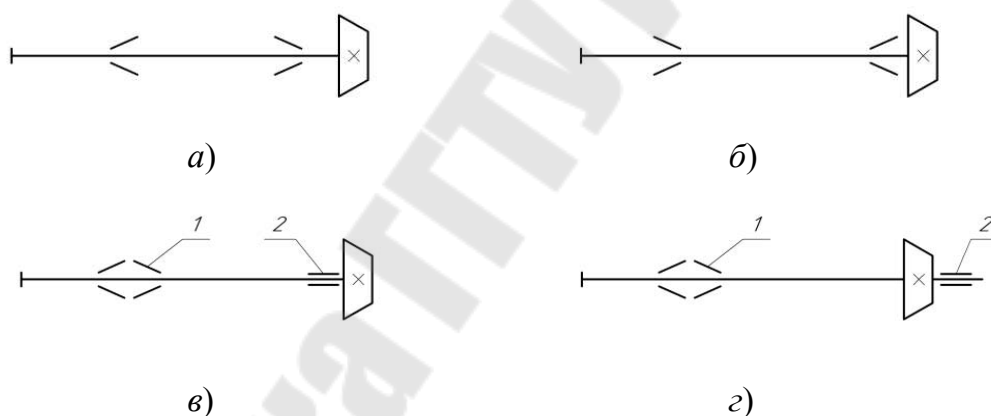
Схемы установки подшипников в опорах валов конических редукторов:
